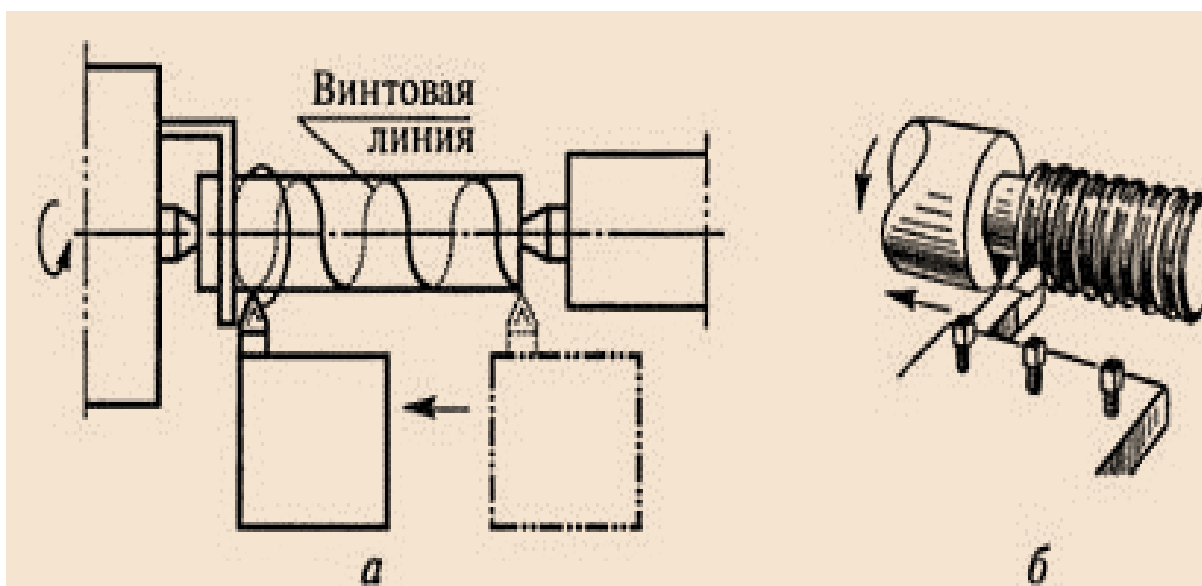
Нарезание резьбы токарным резьбовым резцом:
